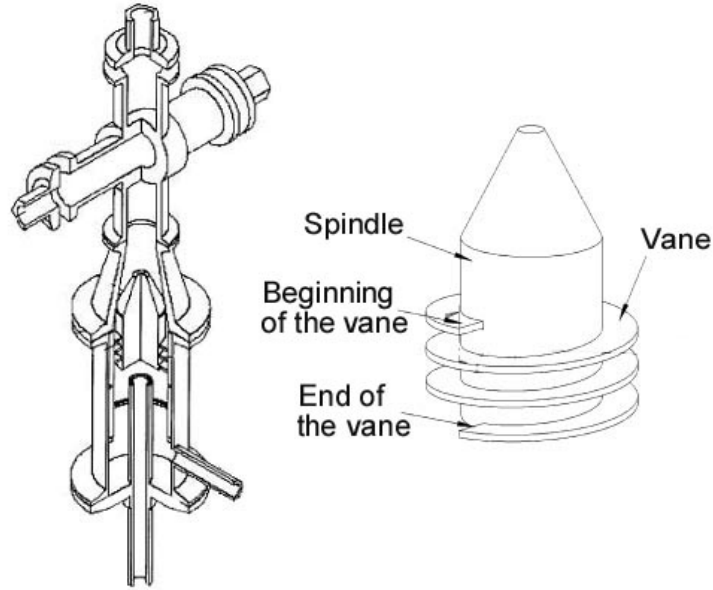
Cyclone axial assemblé. [28, 32].
